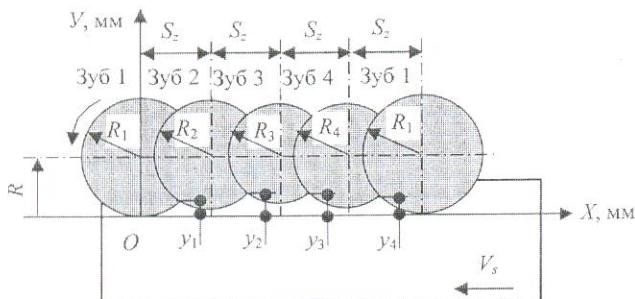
Кинематические волны на фрезерованной поверхности древесины
